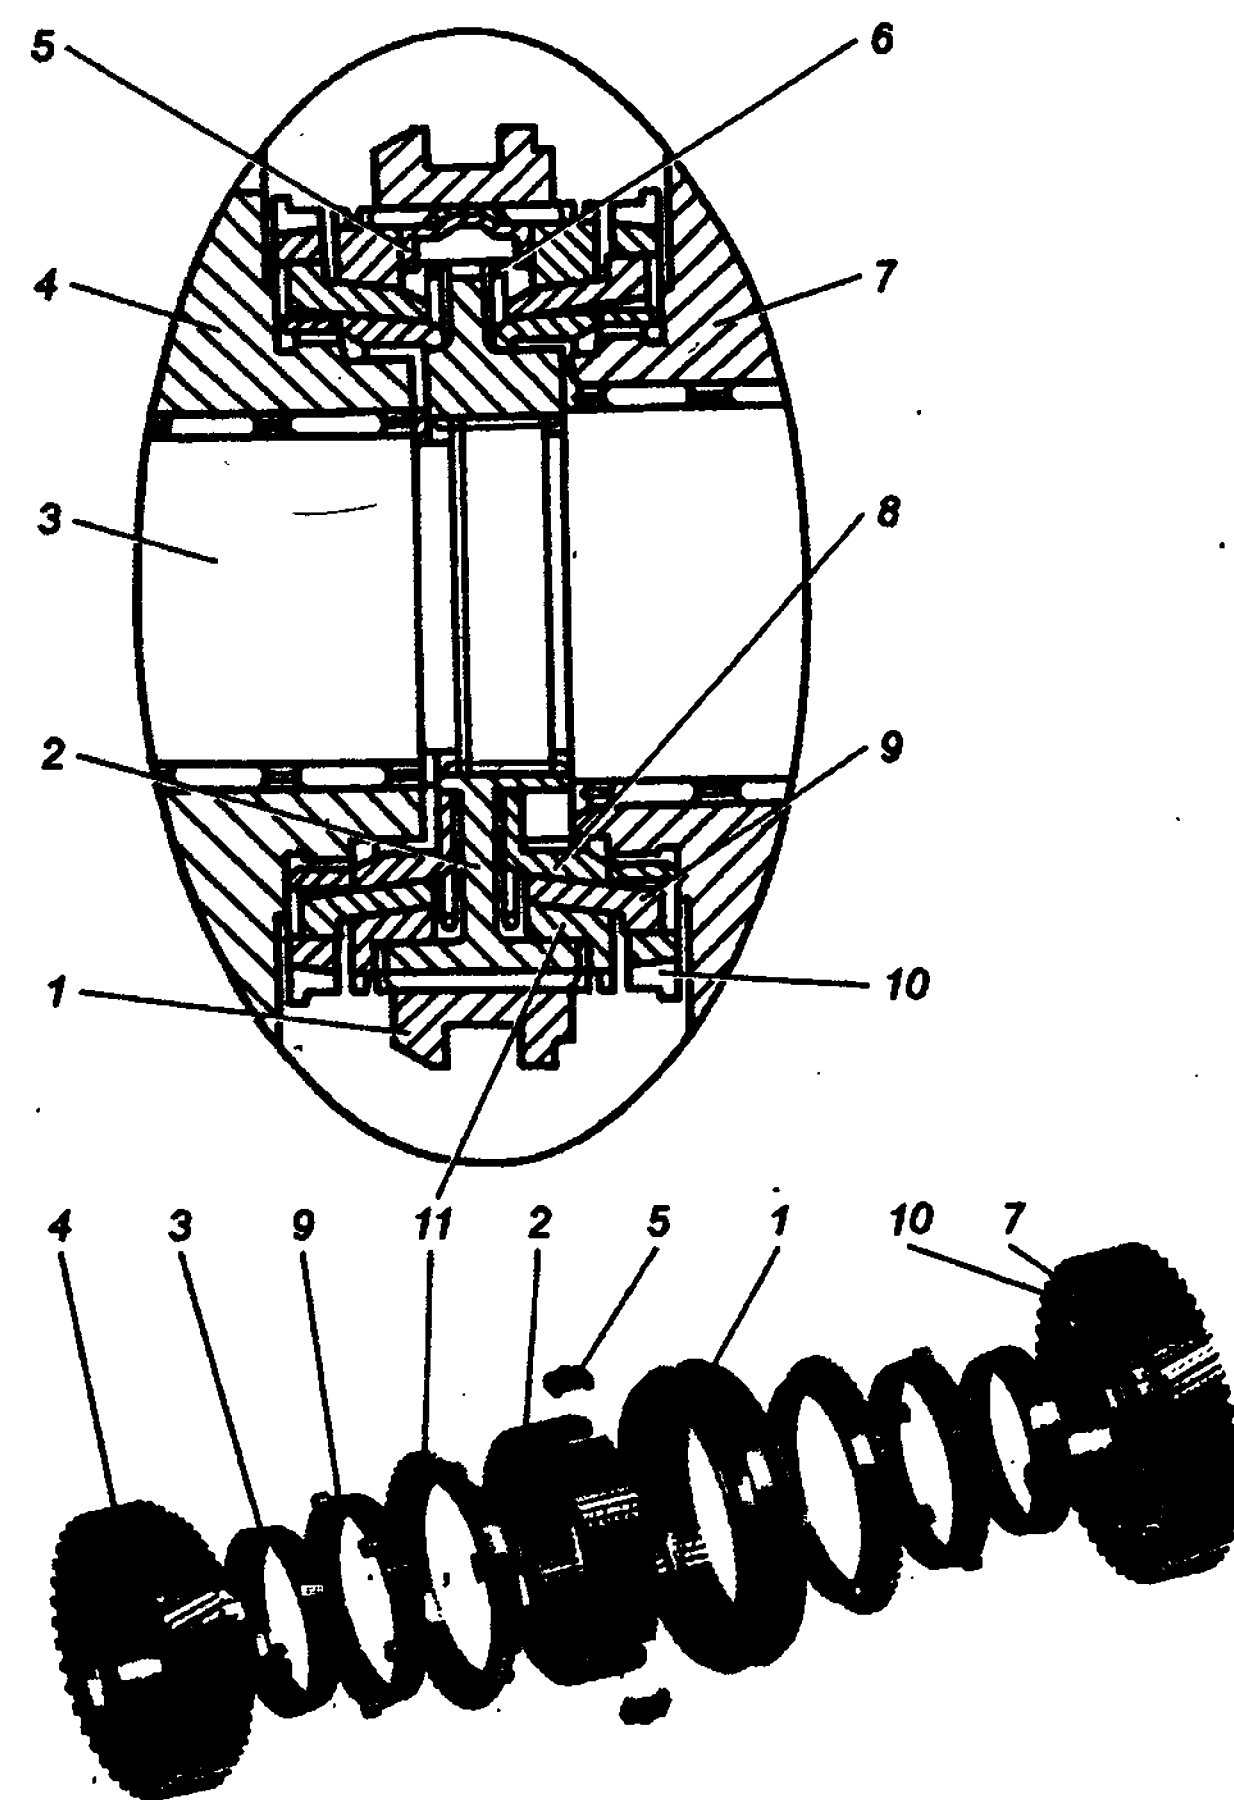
Двухконусный синхронизатор 1-й и 2-й передач: 1 - муфта; 2 - ступица; 3 - вторичный вал; 4 - шестерня второй передачи; 5 - сухарь синхронизатора; 6 - пружина синхронизатора; 7 - шестерня 1-й передачи; 8 - кольцо внутреннее; 9 - кольцо среднее; 10 - зубчатый венец; 11 - кольцо наружное
